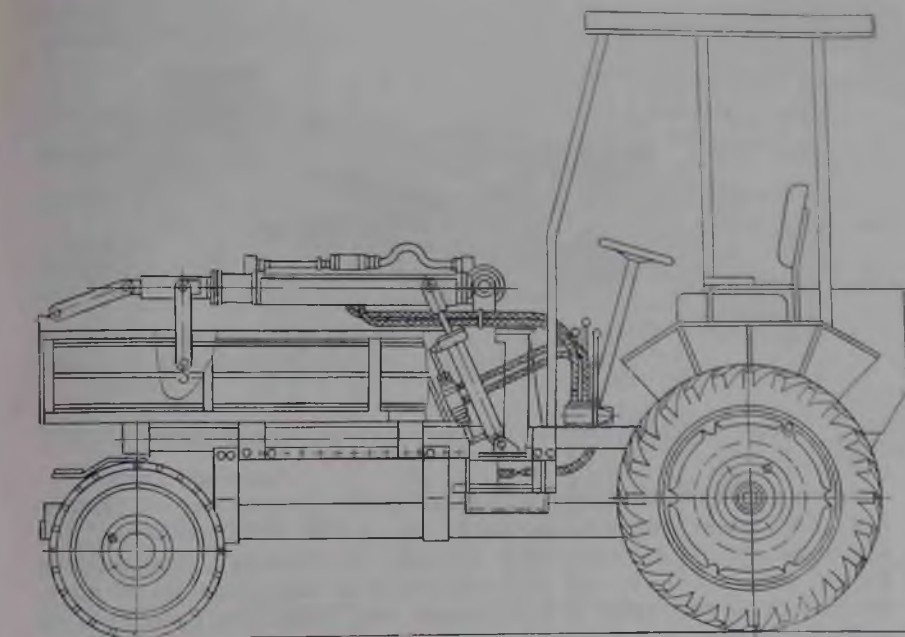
Погрузочно-транспортный агрегат ПСШ-20Д
